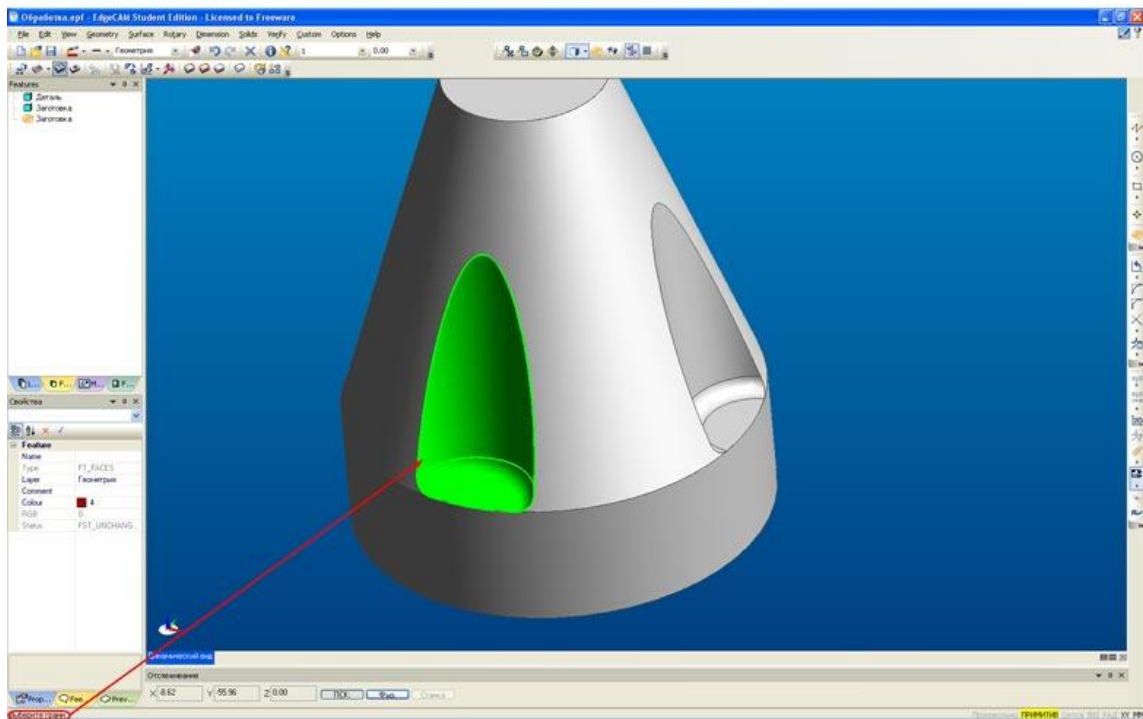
Edgescam. На модели указать поверхности, которые будут фрезероваться
